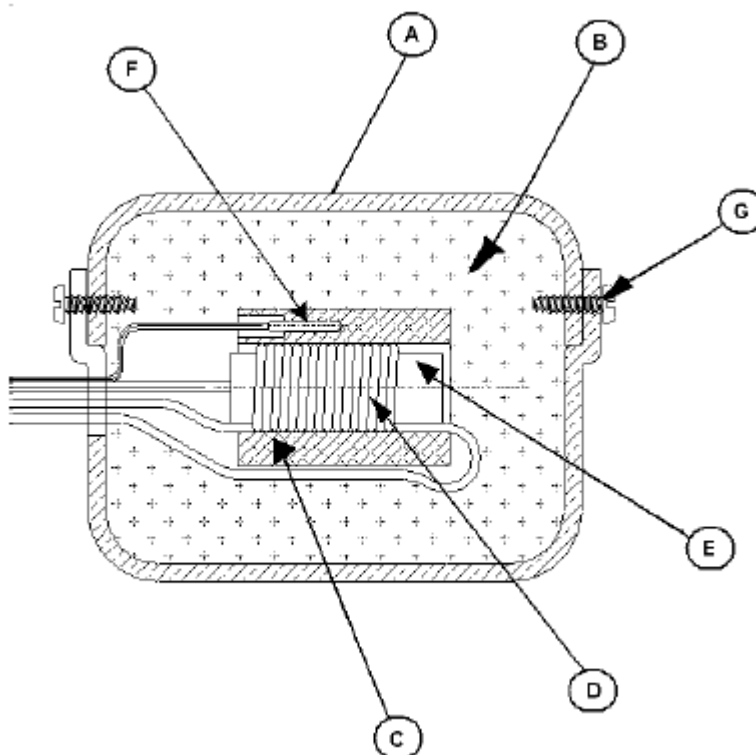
Сборка дополнительного метанатора Модели 700
